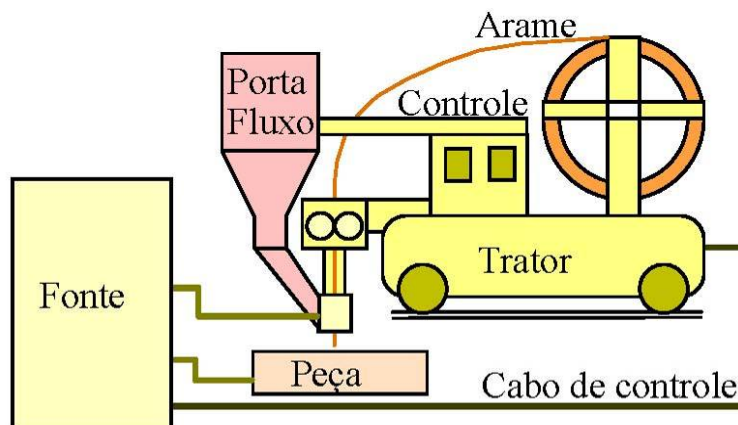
Esquema do equipamento para soldagem a arco submerso
